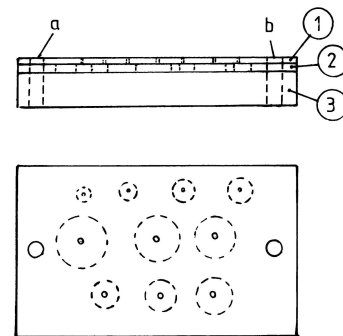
Bohrvorrichtung 1) Bohrschablone, 2) Aufnahmeplatte, 3) Grundplatte, a) Schwenkpunkt, b) Absteckbohrung.
